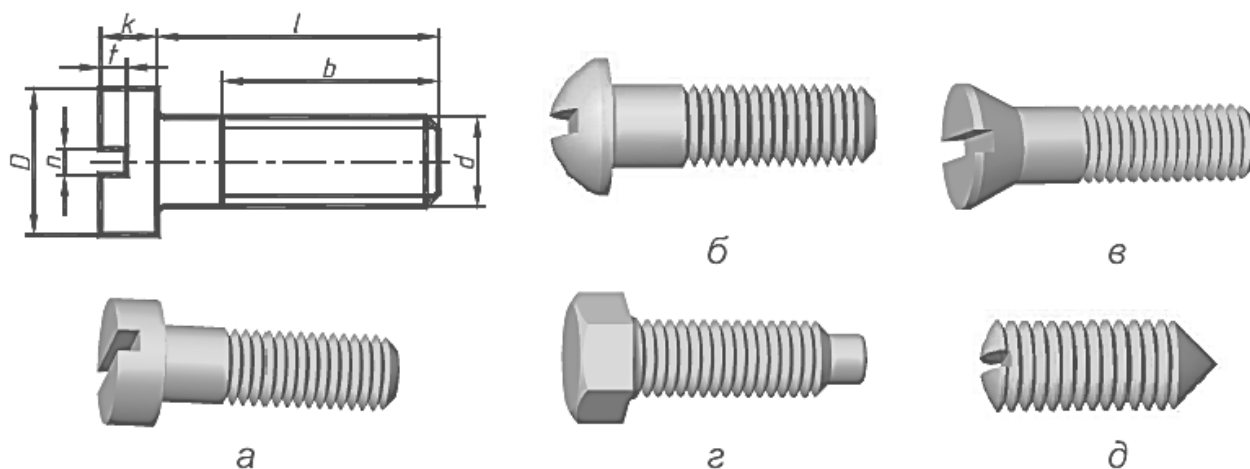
Типы винтов: *а, б, в* – крепёжные; *г* – установочные, *д* – стопорный
